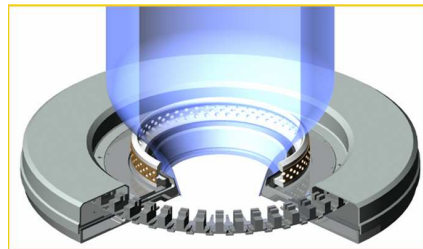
Werkzeug mit Kühlung, 4. Werkzeug mit Kühlung
